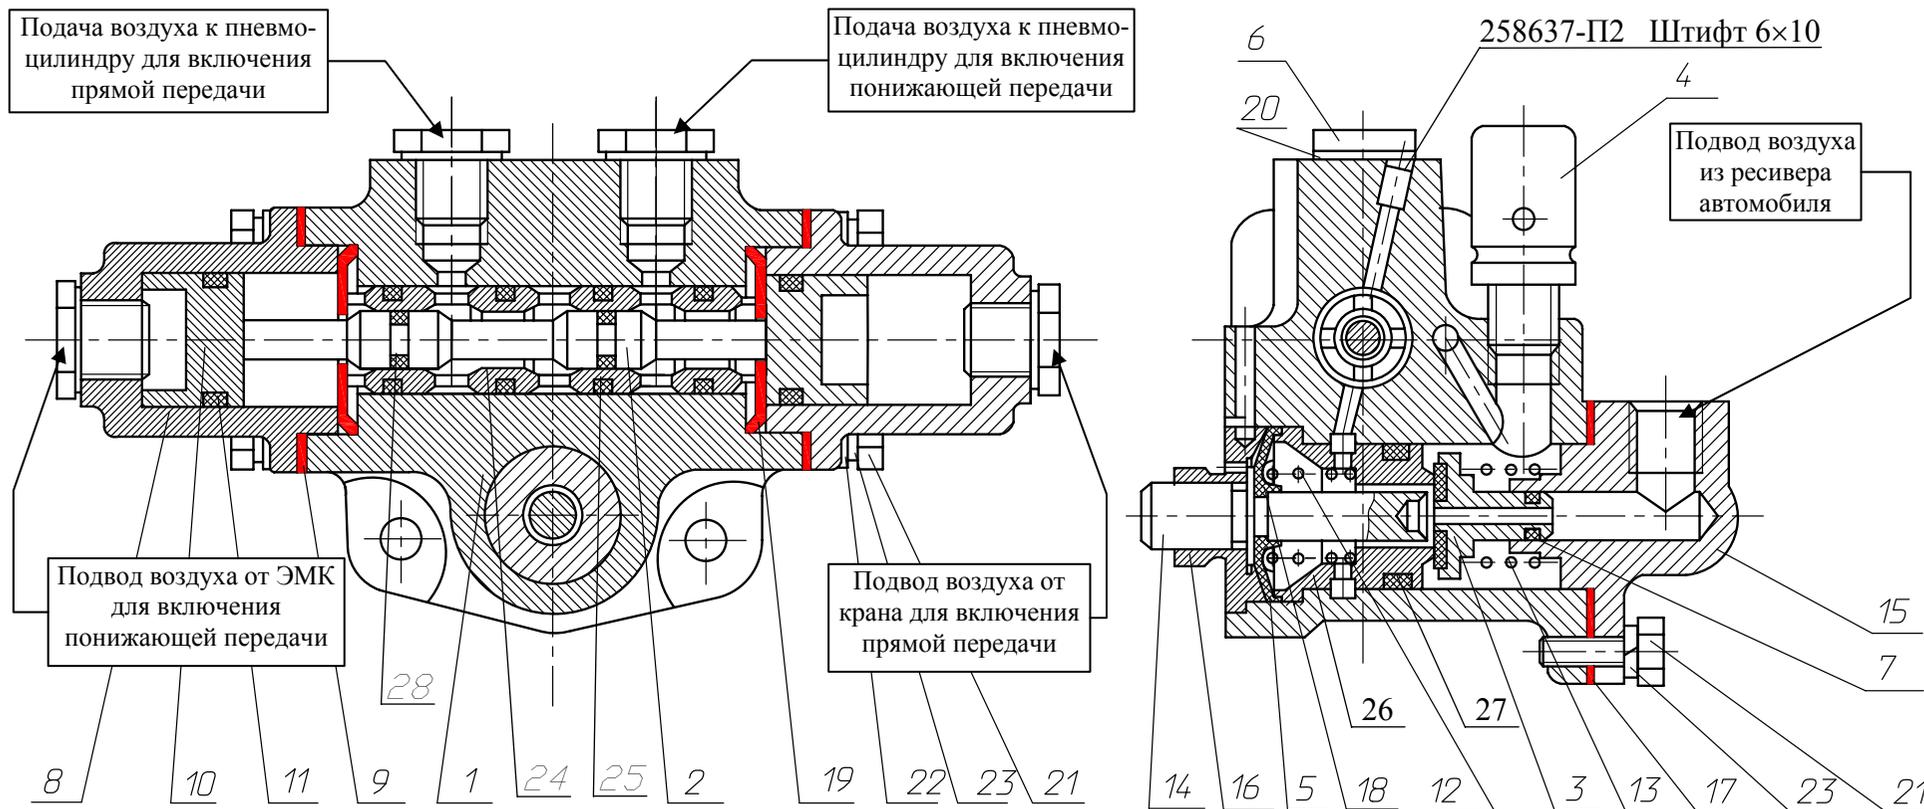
Устройство воздухораспределителя в сборе, 238Н-1723010-01
